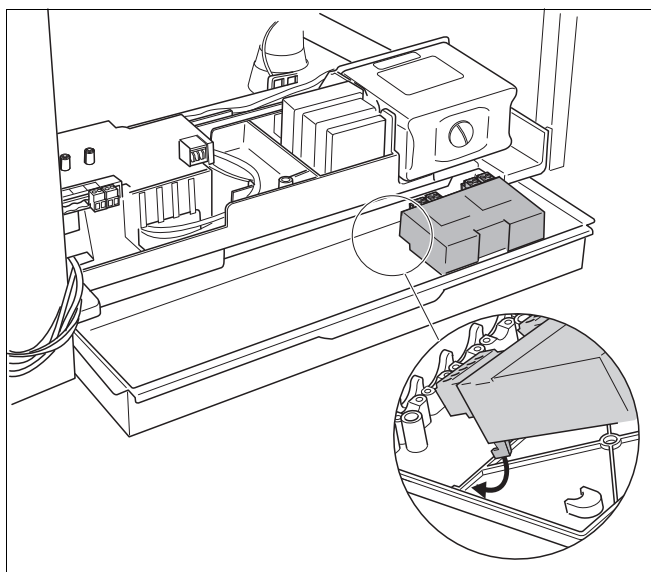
Fissaggio del modulo di funzione nel supporto a muro
